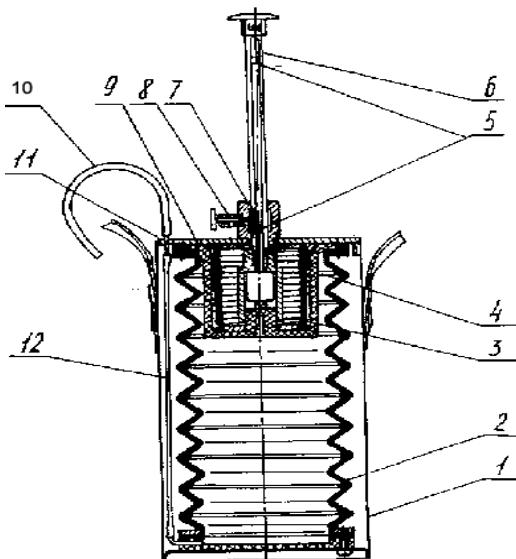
1– Устройство газоанализатора УГ-2: 1 – корпус, 2 – сильфон, 3 – пружина, - кольцо распорное, 5 – канавка с двумя углублениями, 6 – шток, 7 – втулка, 8 – фиксатор, 9 – плата, 10 – трубка резиновая, 11 – штуцер, 12 – трубка резиновая
